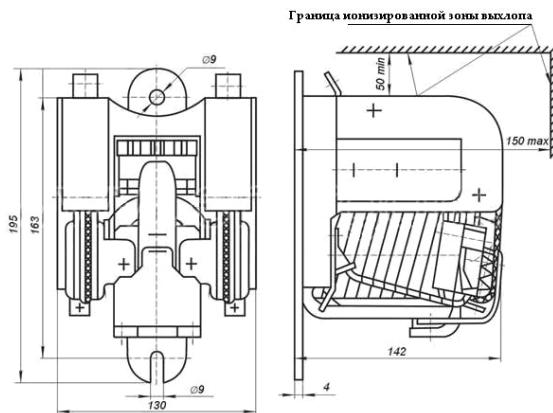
Габаритные, установочные размеры КПД-121 У2
